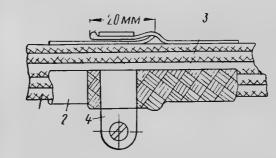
Стык экранирующей плетенки с трубопроводом:
